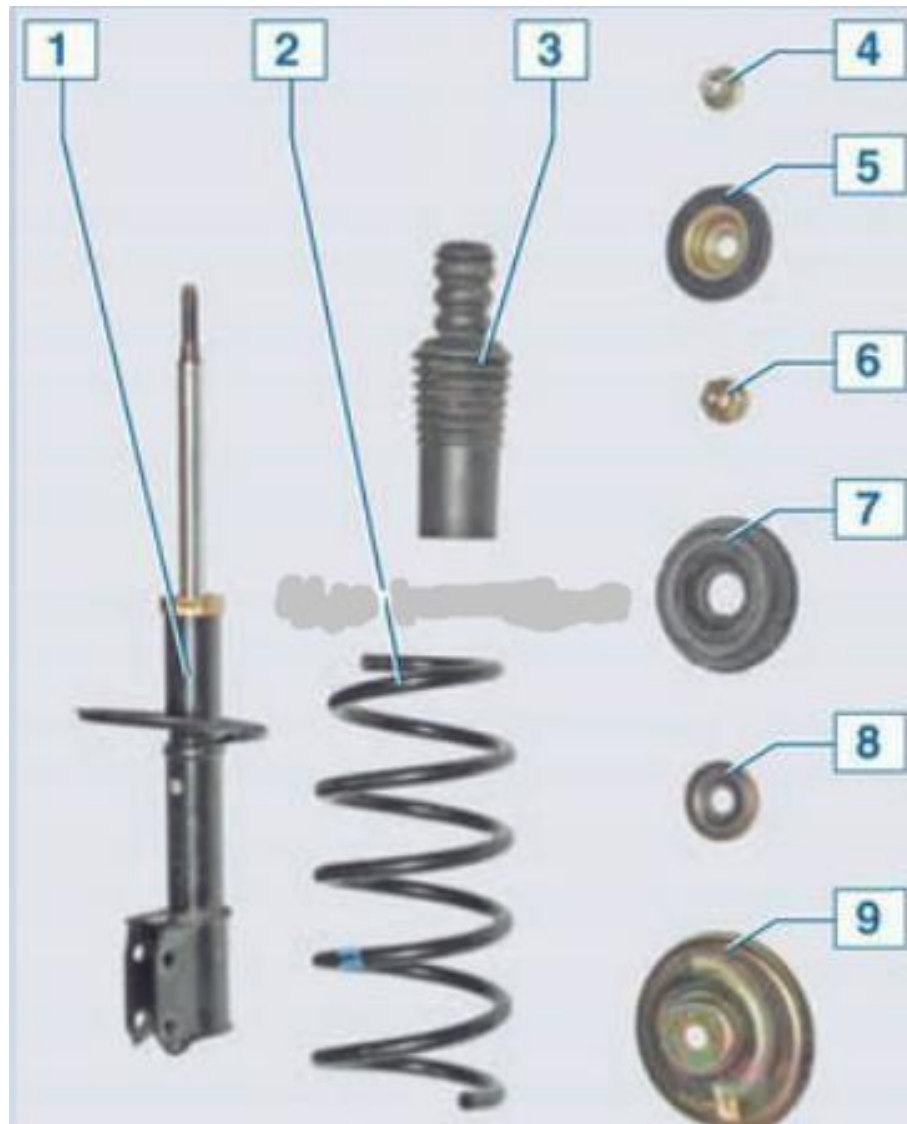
Конструкція передньої амортизаторної стійки
